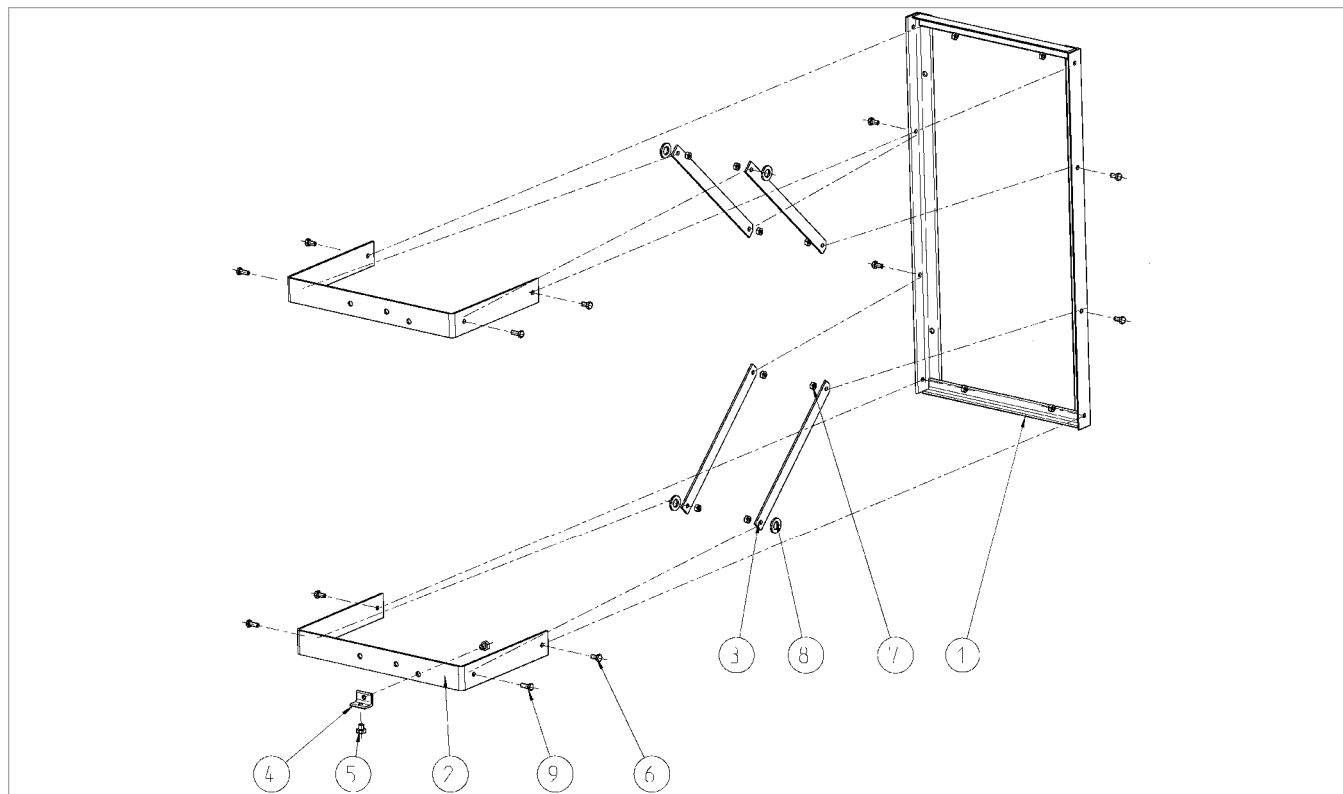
Plano de ensamblaje de la consola mural WK-WWS-24
